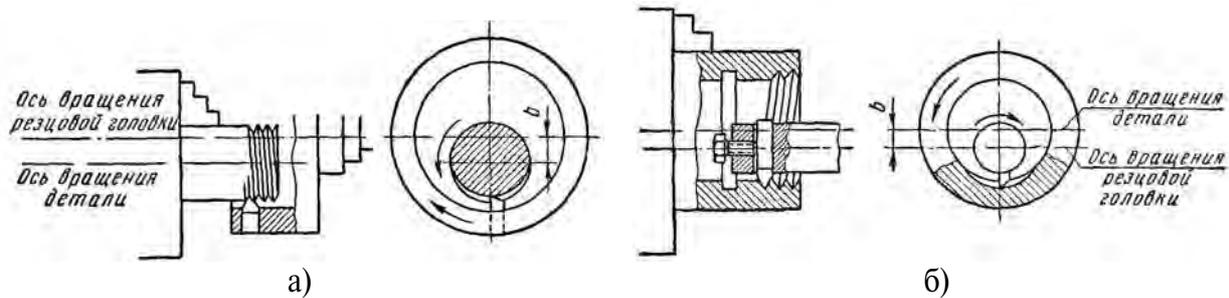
Схема нарезания резьбы вращающейся резцовой головкой:
